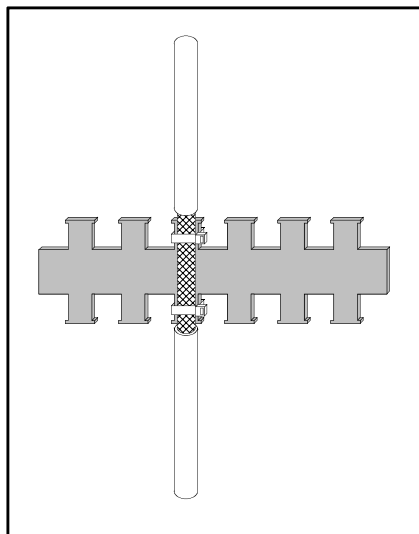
с: Металлический рукав или компонент кабеля крепится на металлическую пластину/ зубчатую шину (гребенку)
